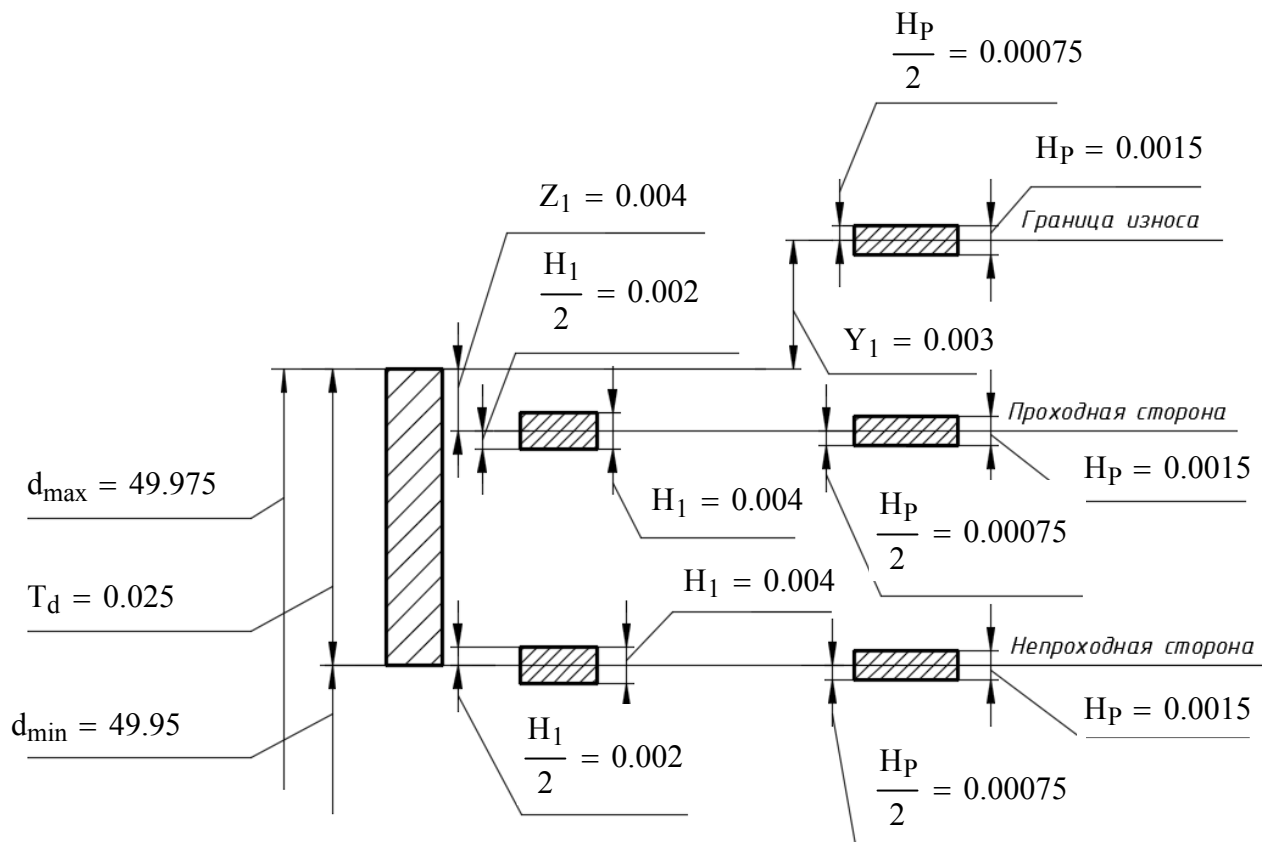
Схема расположения полей допусков калибра-скобы
